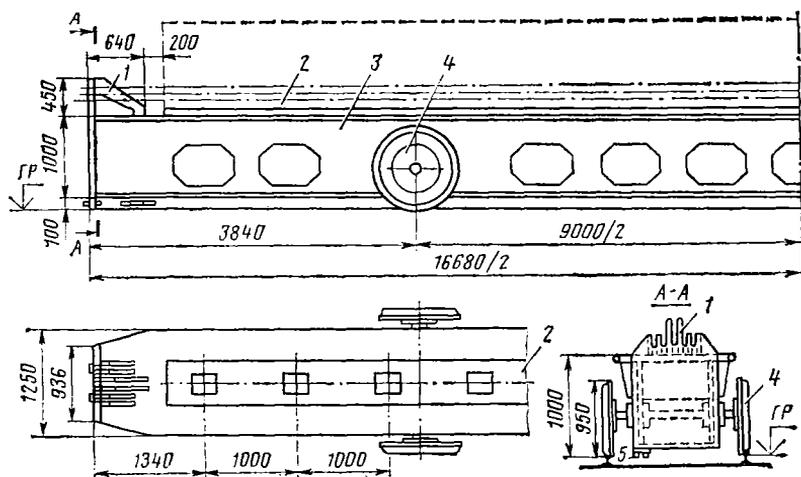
Подвижной упор для балок с горизонтальной арматурой длиной 15 м: 1 — гребенка; 2 — поддон; 3 — распорная балка; 4 — тележка; 5 — улавливающее устройство
